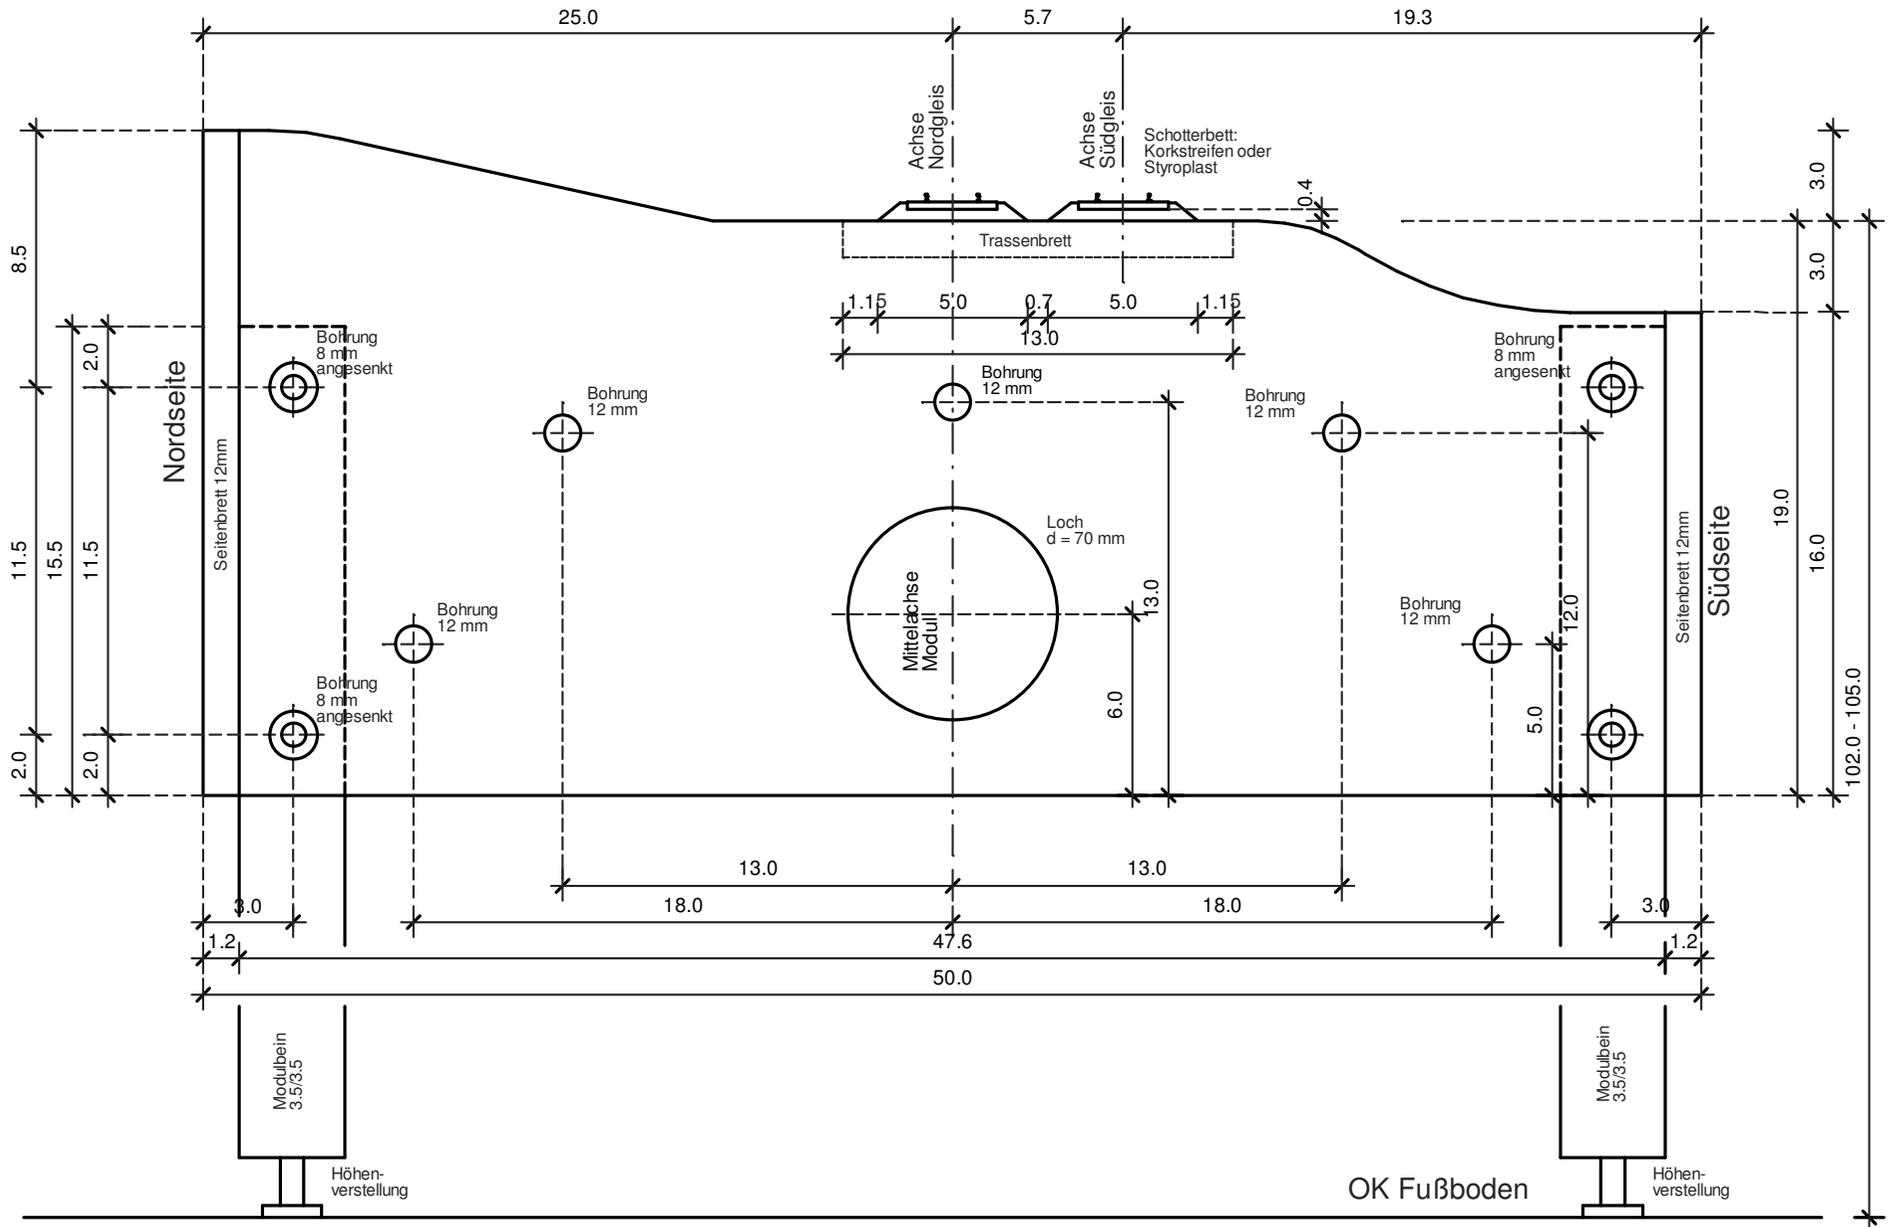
Modulanschluss / Stirnbrett – Maßstab 1 : 2.5 - alle Maße in cm
